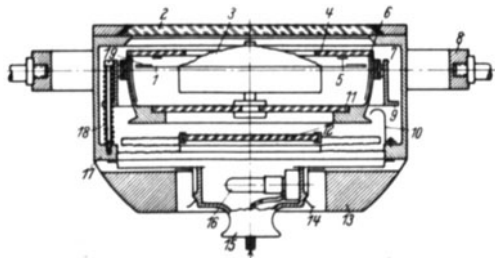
1 Rose, 2 äußerer Glasdeckel, 3 Schwimmer, 4 innerer Glasdeckel, 5 Abblendering, 6 Steuerstrich, 7 Tragring für Federn, 8 Kardanring, 9 Ring, in dem die Kardanaufhängung des Innenkessels gelagert ist, 10 Ausschlagfedern, die verhindern, daß die Ausschläge des Innenkessels zu groß werden, 11 innerer Glasboden, 12 äußerer Glasboden, 13 Beschwerung, 14 Federklammer für Lampenkasten, 15 Handgriff, 16 Lampe, 17 äußerer Kompaßkessel, 18 Federn, 19 innerer Kompaßkessel.
